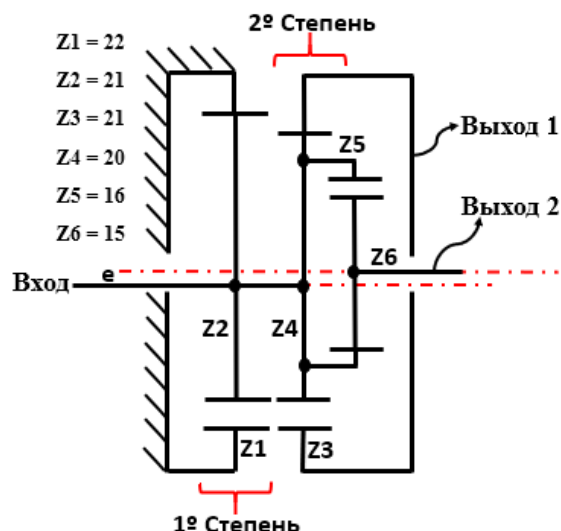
Кинематическая схема коробки передач с двумя коаксиальными выходами скорости.
